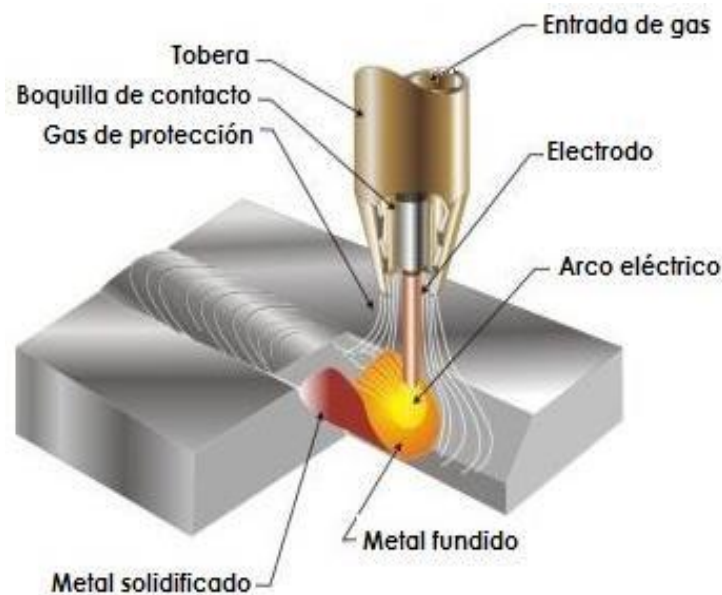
Proceso de Soldadura GMAW [11]
